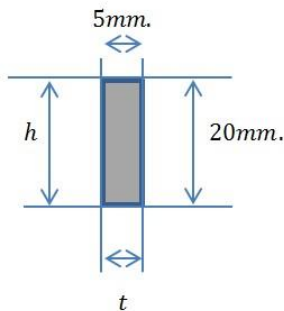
dimensiones de la leva menor vista de perfil parte baja.
